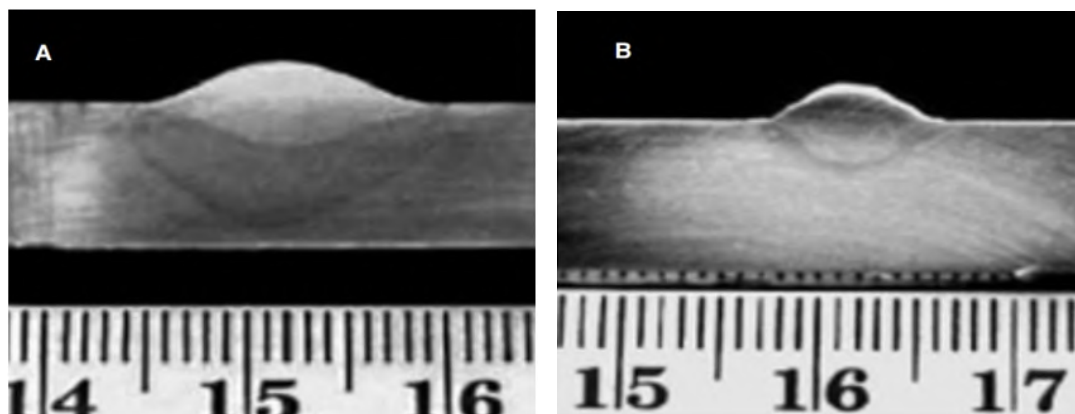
Macrografías de una muestra de soldadura A y B : Secciones transversales del cordón de soldadura (Nguyen et al., 2004).
